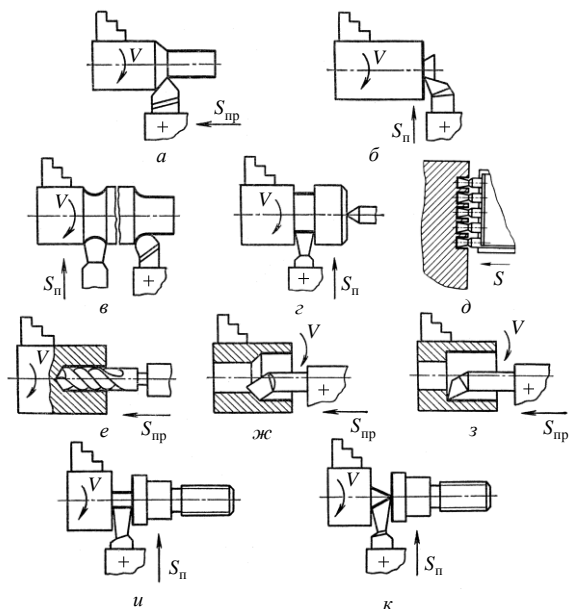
Схема обработки заготовок на токарно-винторезном станке: *а* — обтачивание конических и цилиндрических поверхностей; *б* — подрезание торцов; *в–д* — точение канавок и галтелей; *е* — сверление отверстий; *ж, з* — растачивание отверстий; *и, к* — отрезание
